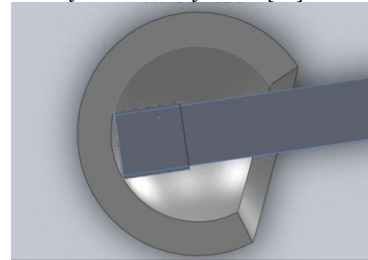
Схематичне зображення протезу стегнової головки з кераміки Al_2O_3 на металевій шийці ніжки штучного суглоба [6]
